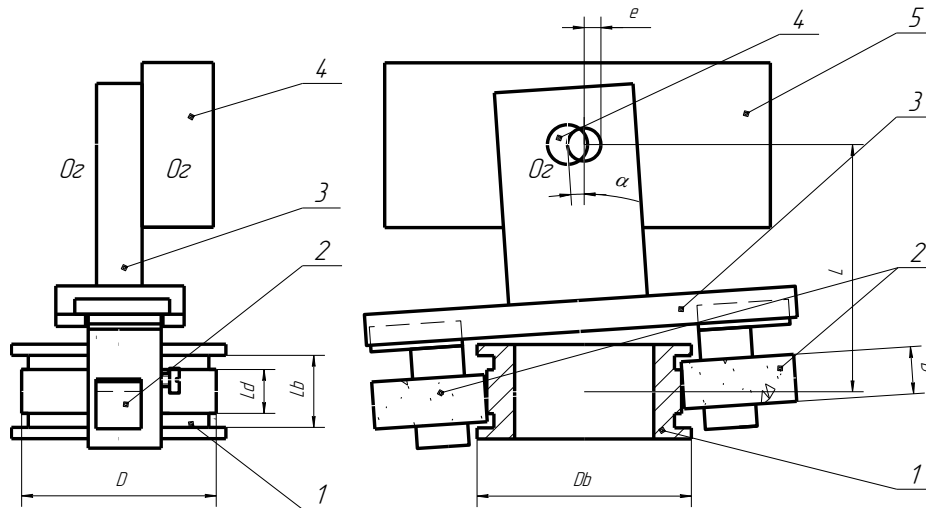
Схема эксцентрикового суперфиниширования внутреннего кольца роликоподшипника
